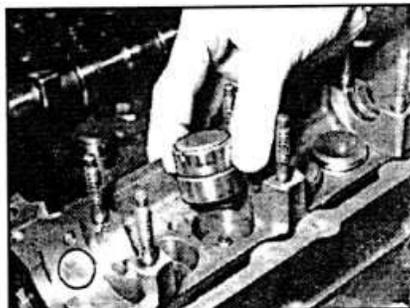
E.16. Извлечение толкателя с пластиной регулировки зазора клапана.
